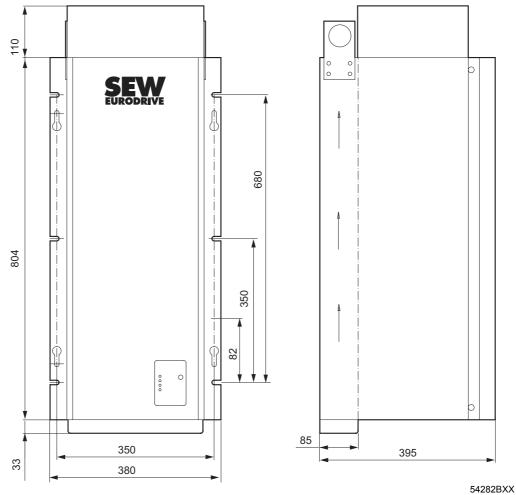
Dimensões do MDR60A do tamanho 6, dimensões em mm
